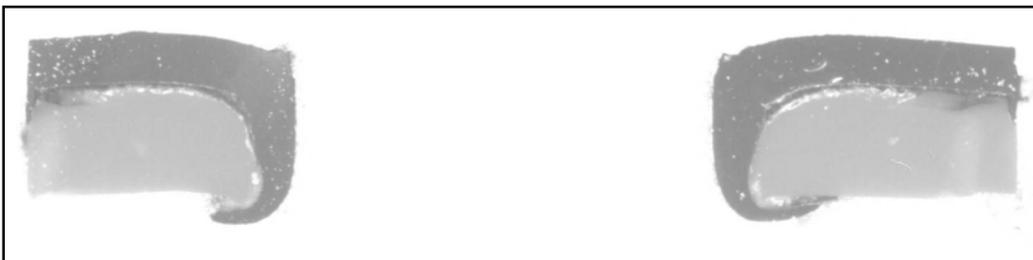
Makroschliff einer Stahlblech- GfK-Verbindung mit dem Fließbohrnieten.
